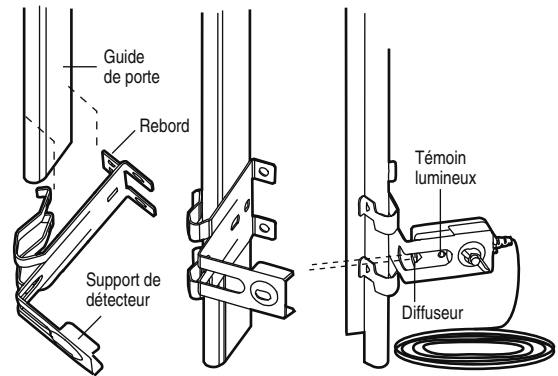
MONTAGE MURAL (CÔTÉ DROIT)
